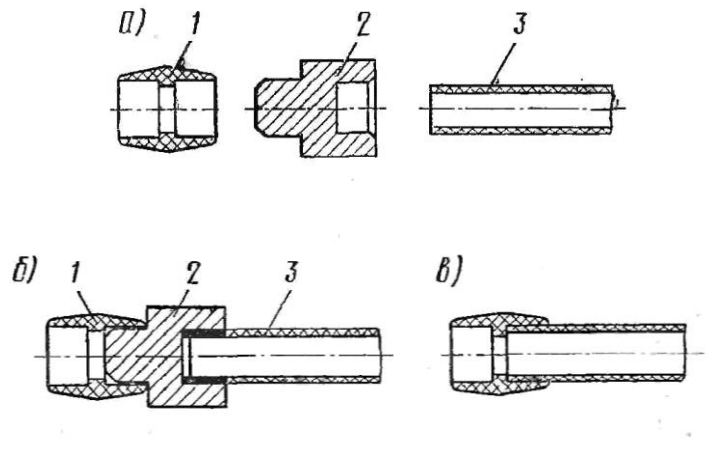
Последовательность сварки трубы с муфтой контактным нагревом: а – положение элементов до нагрева; б – положение соединяемых элементов при нагреве; в – сварное соединение; 1 – муфта; 2 – нагреватель; 3 – труба
